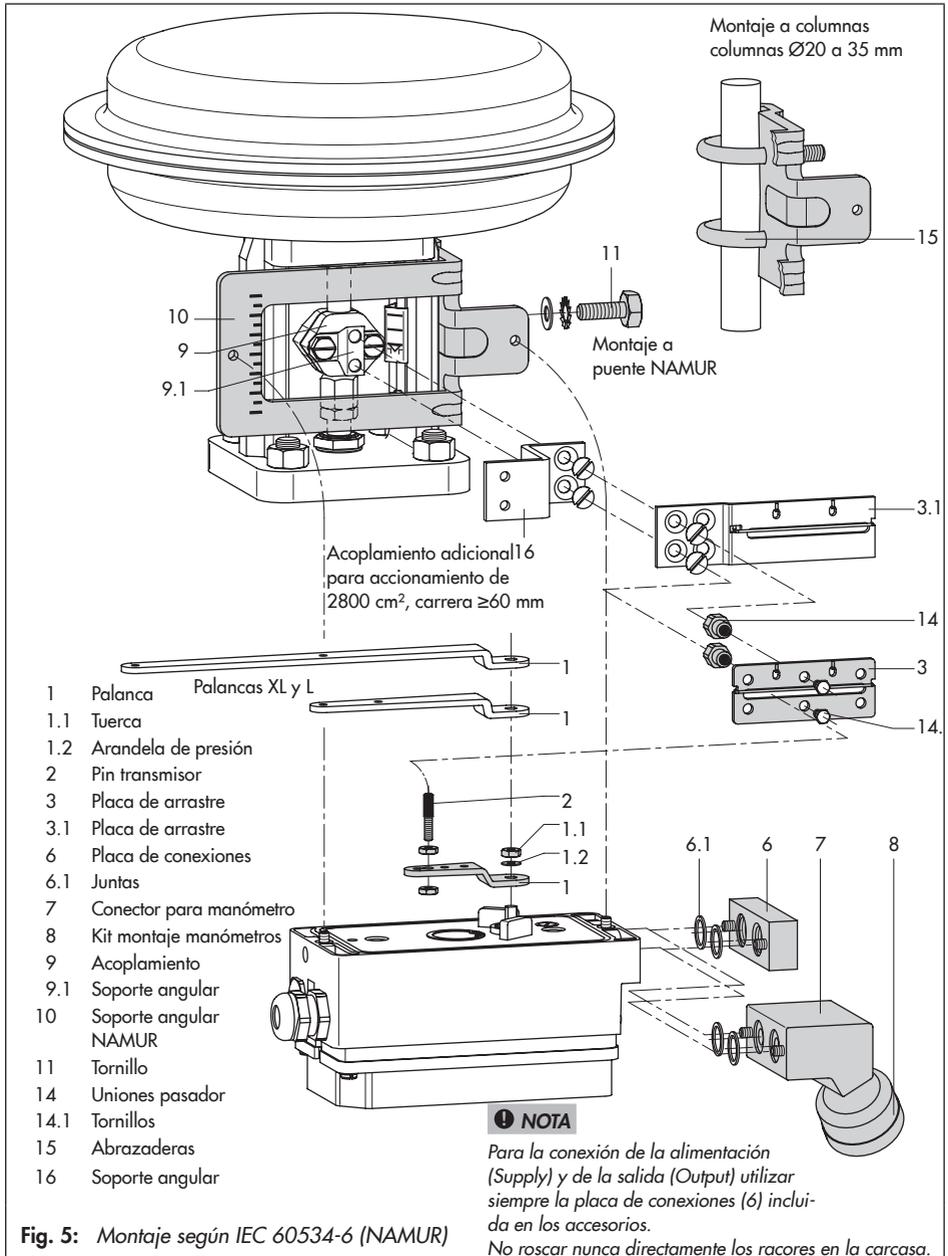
Montaje según IEC 60534-6 (NAMUR)
